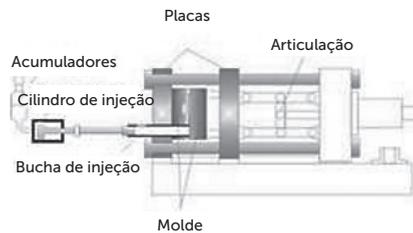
| Ilustração de máquina de fundição sob pressão em câmara quente
